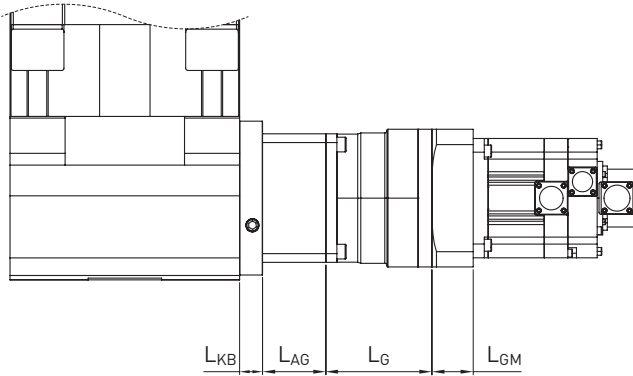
Motoranbindung Lineartisch HT-B mit Getriebe
